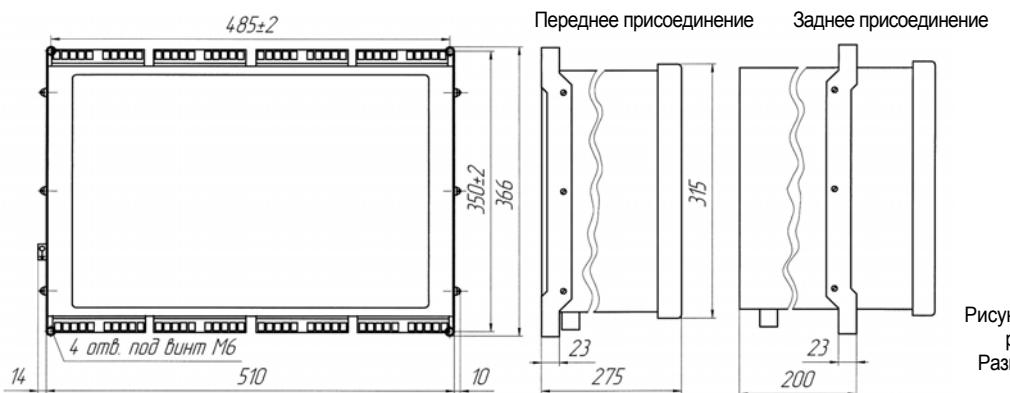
Габаритные, установочные размеры блока типа БЭ 8302М
